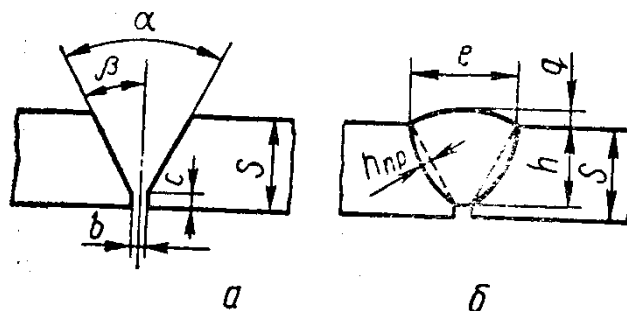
Елементи геометричної форми підготовлених кромок під зварювання (а) та виконаного шва (б)
